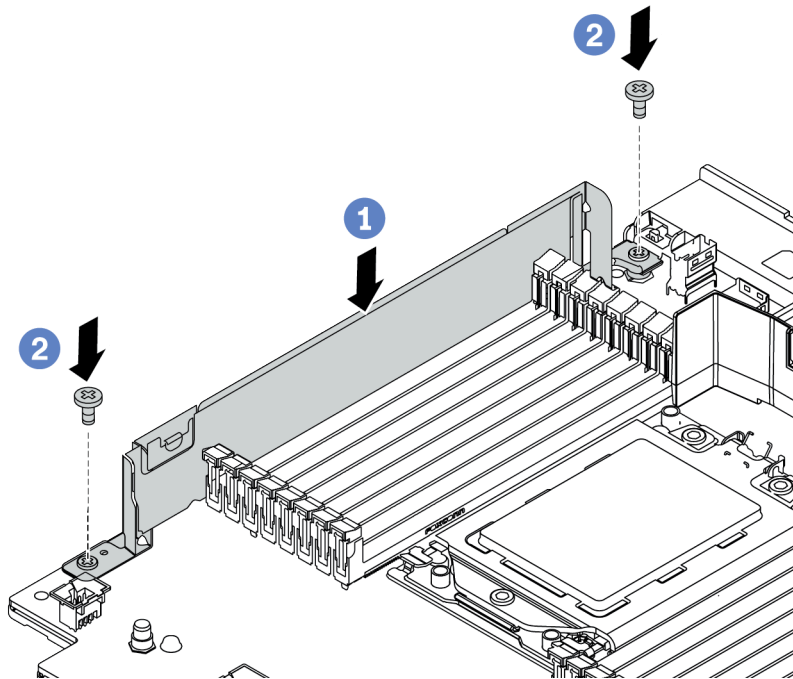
Installazione della staffa per il montaggio a parete con cavo
